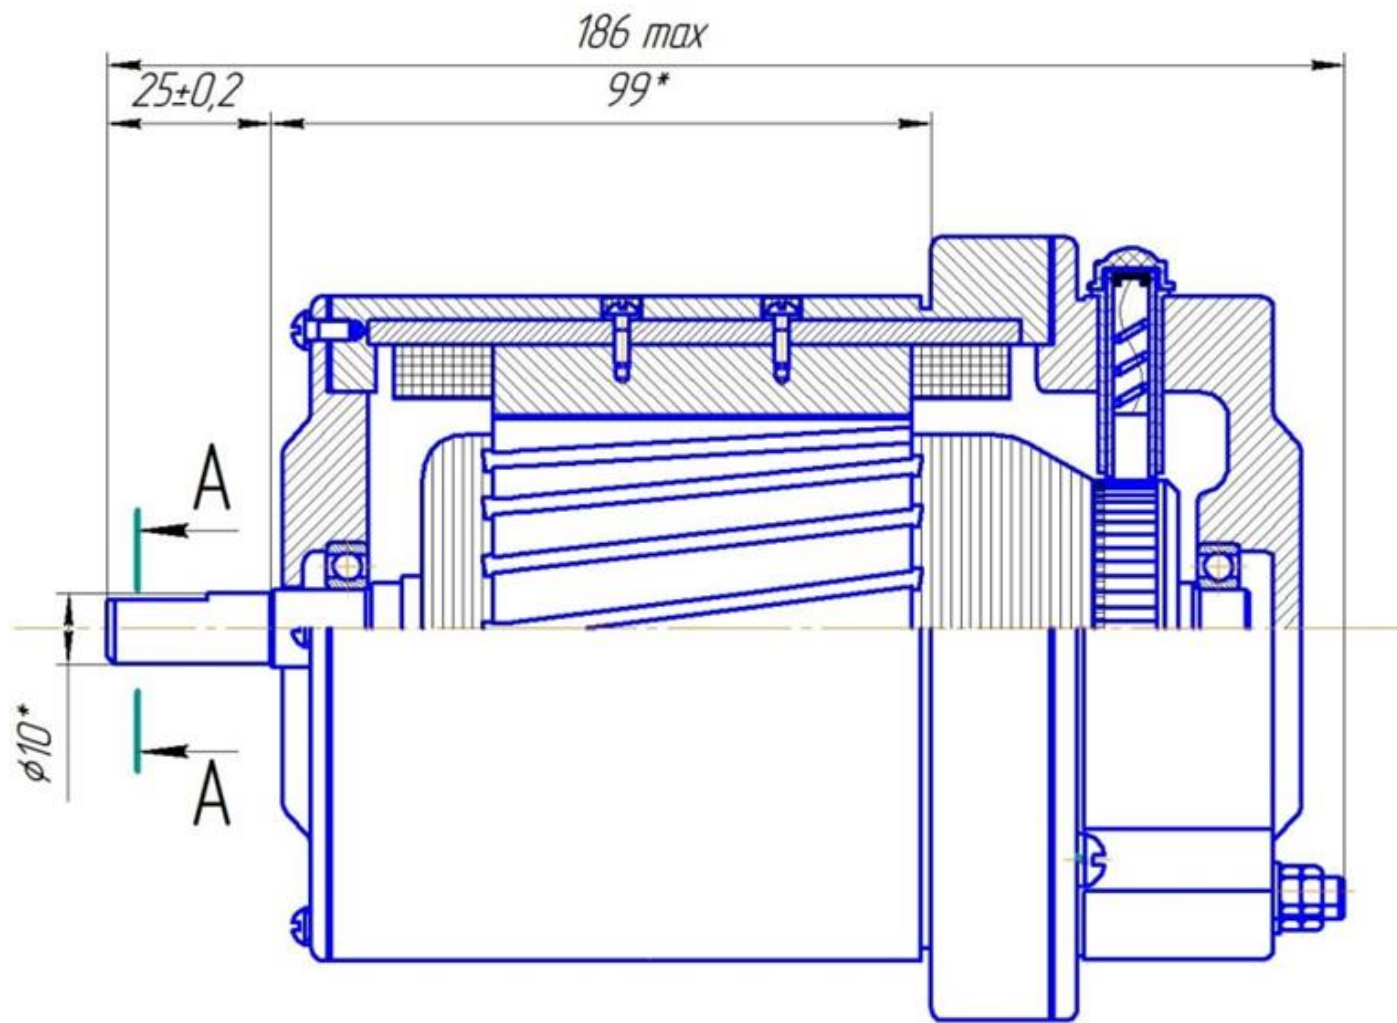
Общий вид двигателя постоянного тока (продольный разрез)
